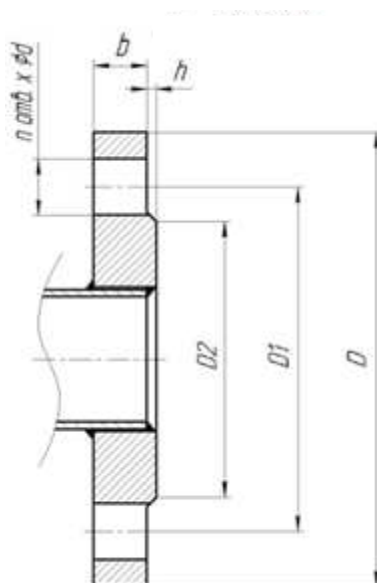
Присоединительные размеры фланцев расходомера и КМЧ
